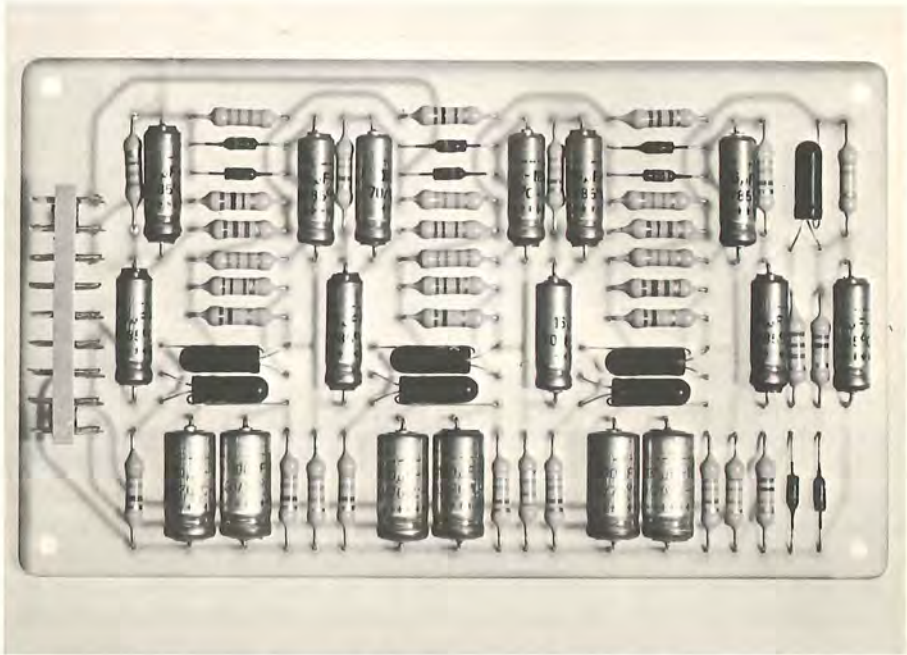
Schakeling van foto 4, uitgevoerd met gedrukte bedrading
